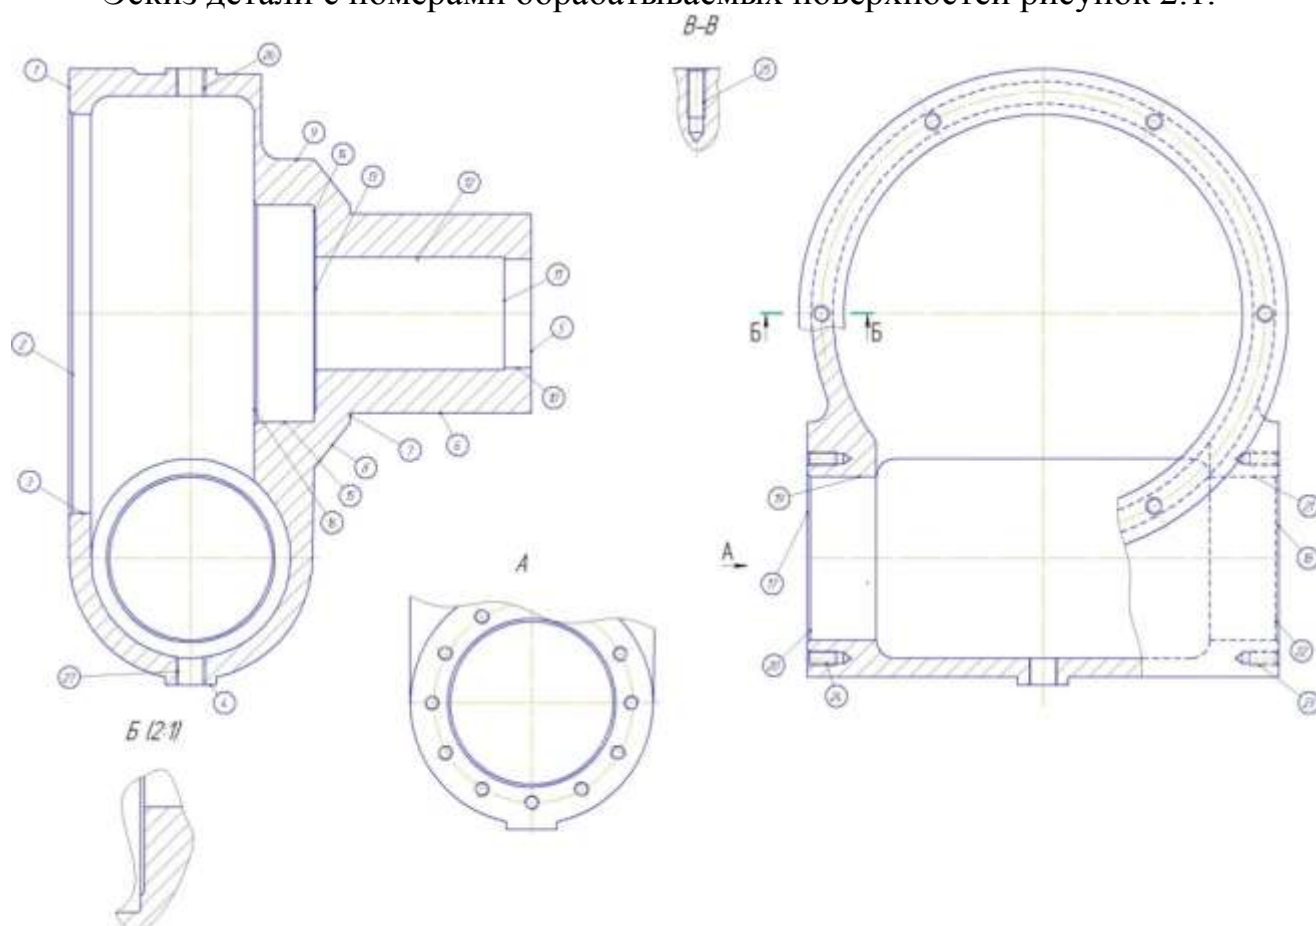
Эскиз детали с номерами обрабатываемых поверхностей
